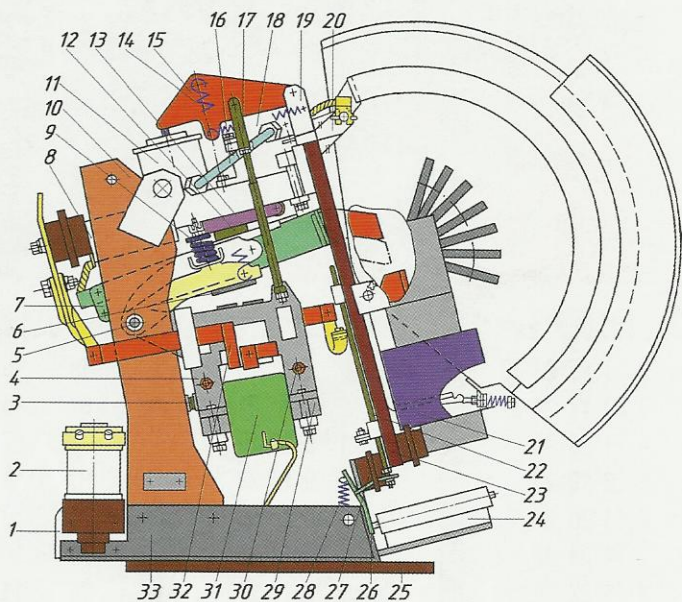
Конструкция быстродействующего выключателя ВБ-11:
